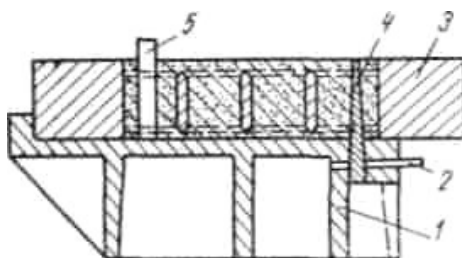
Плита для формовки литниковой системы в верхней опоке
